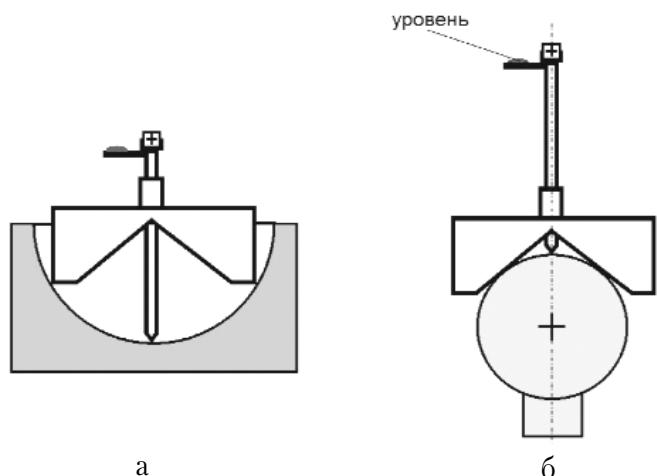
Измерение посадочного места подшипника (а) и образующей ролика (б)
